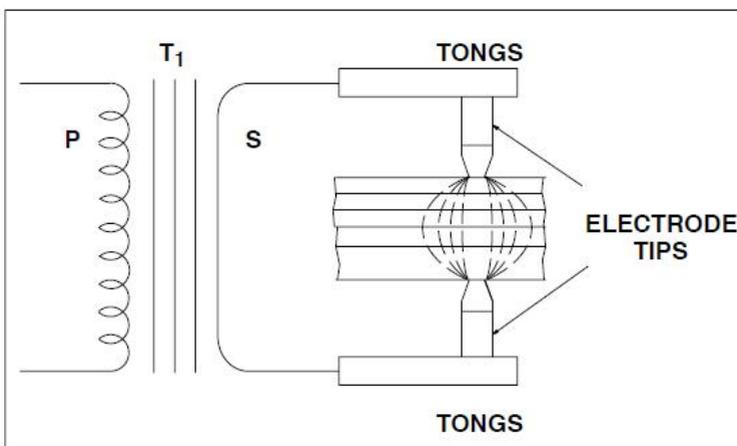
Widerstandspunktschweiß-Wärmezonen
